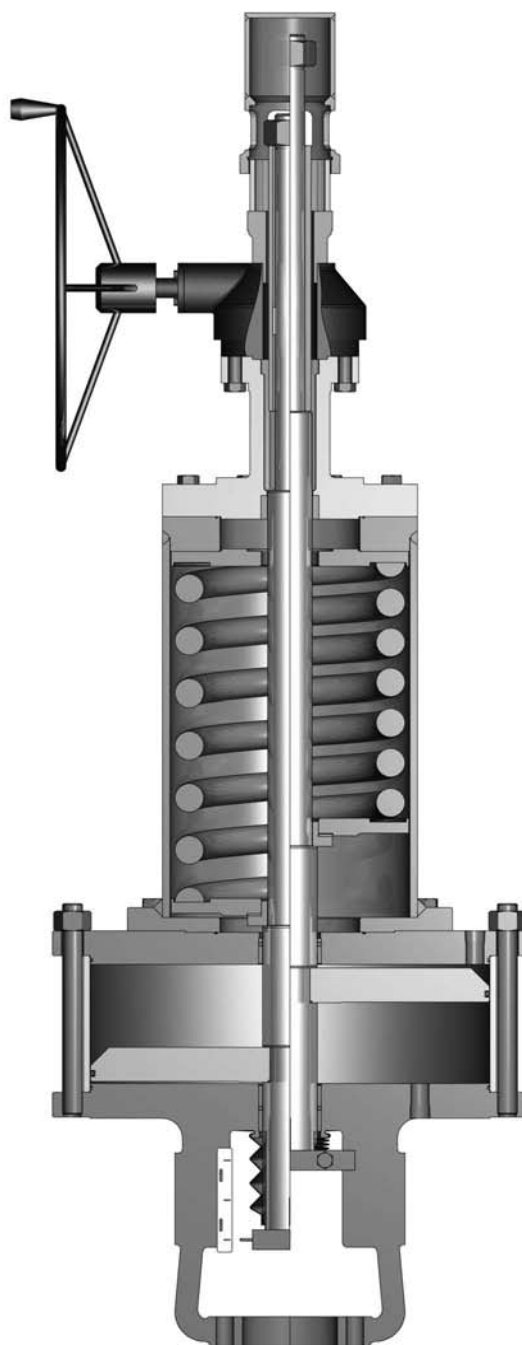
Установка поставляемого по заказу привода с конической зубчатой передачей
